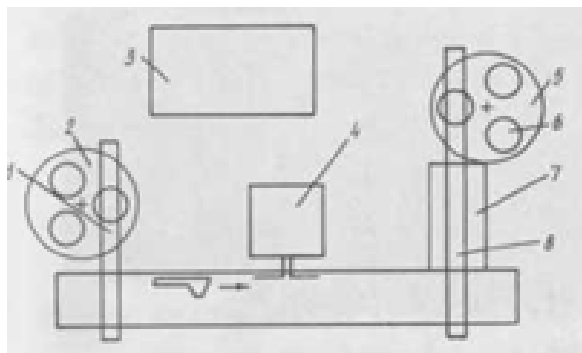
Схема модуля индукционной наплавки односторонних лап культиватора
